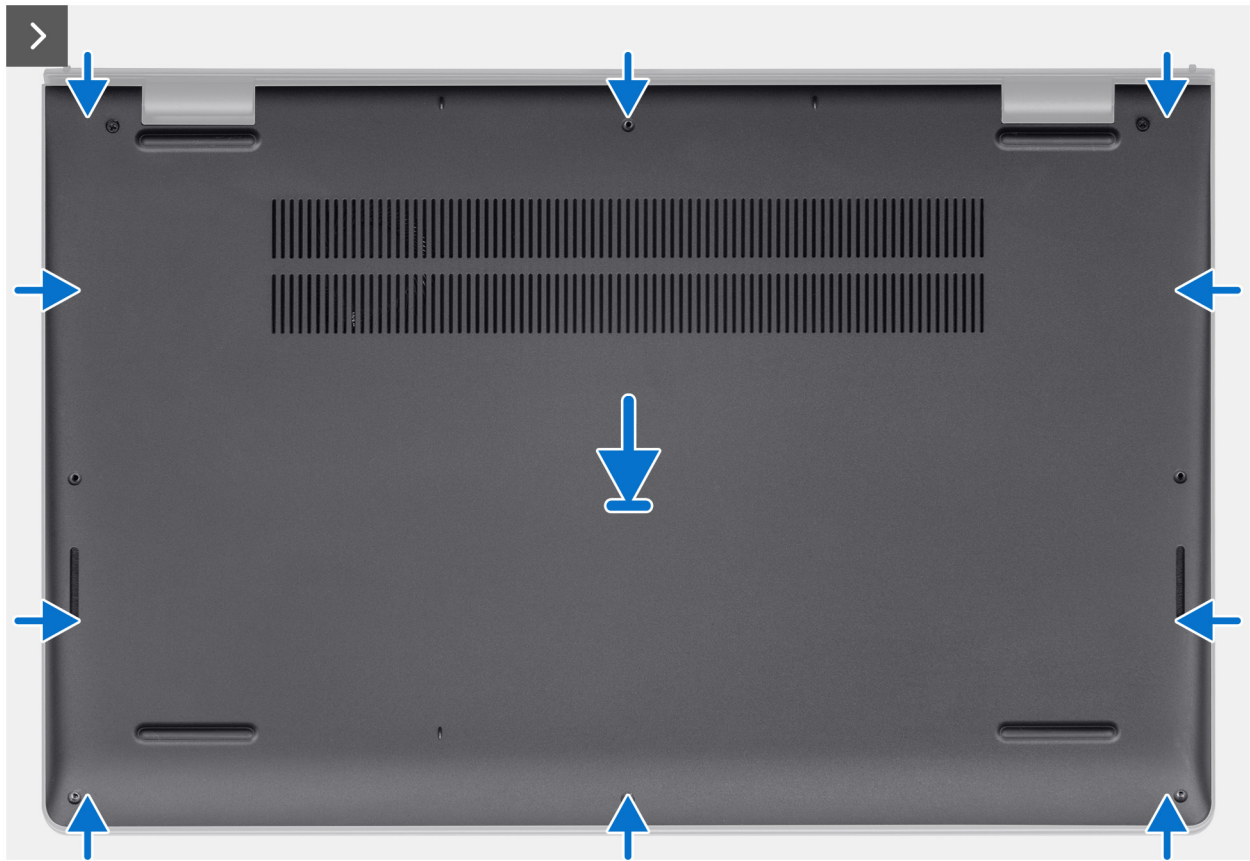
Coloque la cubierta de la base sobre el ensamblaje del teclado y el reposamanos.
